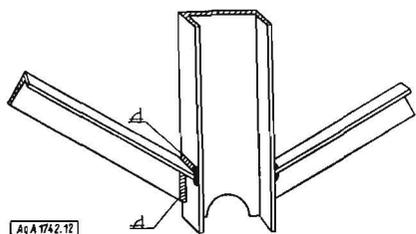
Verbindung von Winkelprofilen, schweißgerechte Ausführung
